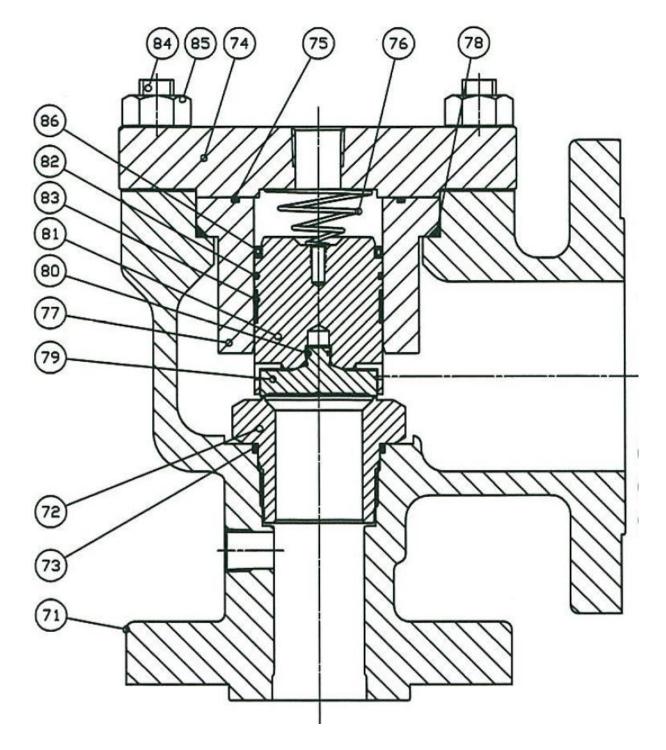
Главный клапан 3900 MPV с уплотнением седла металл по металлу в сборе
